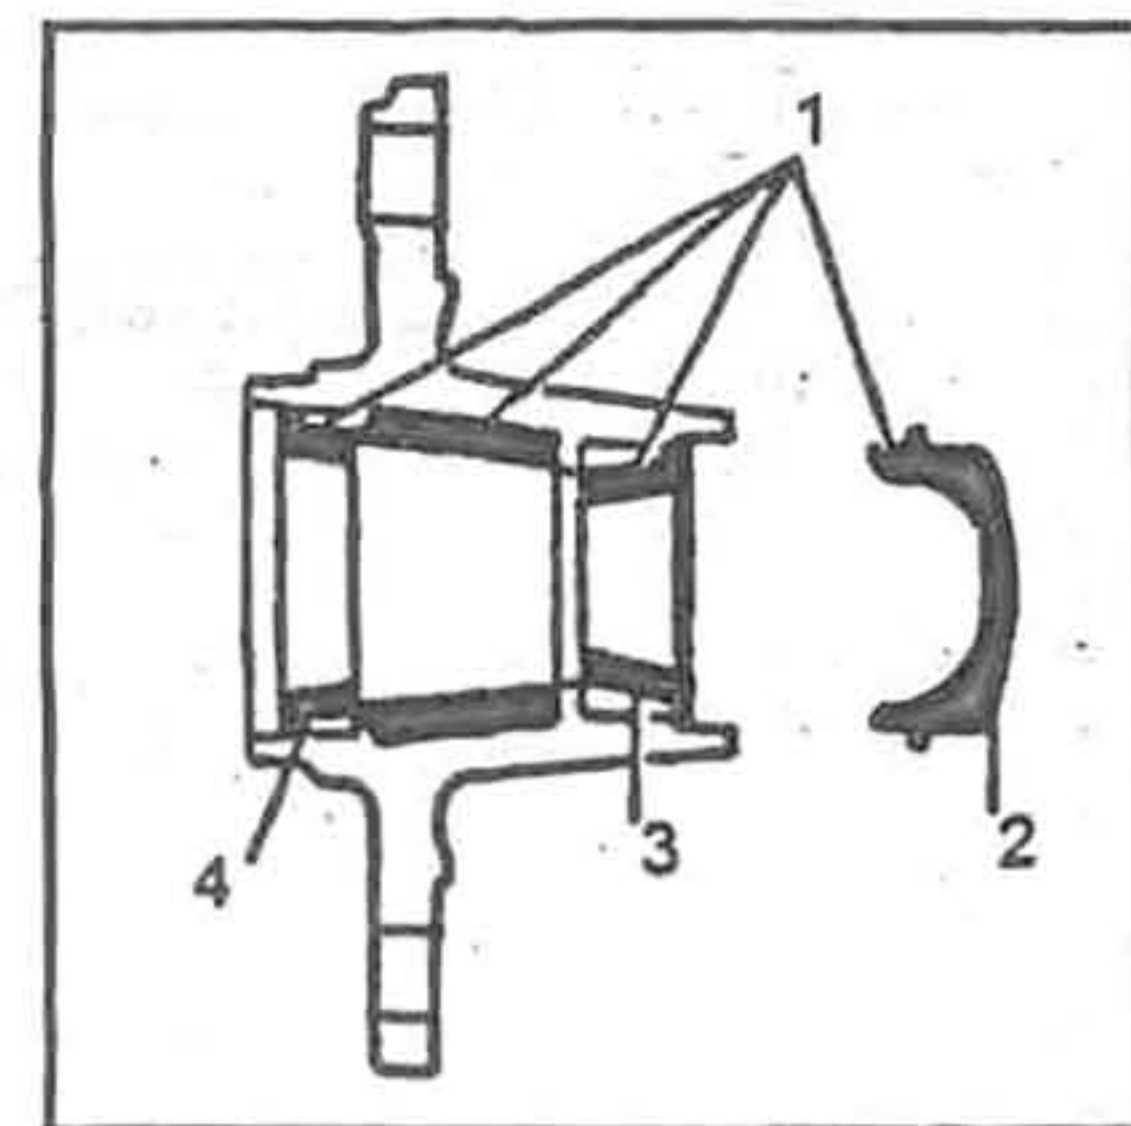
1. Места нанесения универсальной консистентной смазки. 2. Крышка. 3. Наружный подшипник. 4. Внутренний подшипник.
